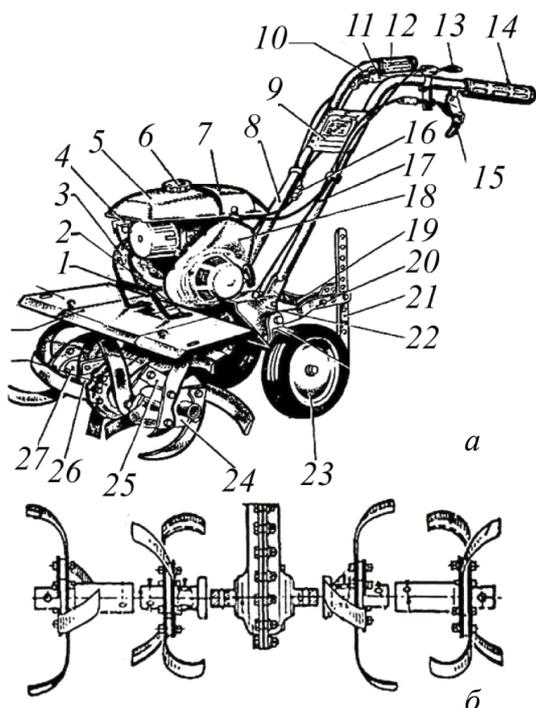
Мотокультиватор «Крот»: а – схема; б – рабочий орган
